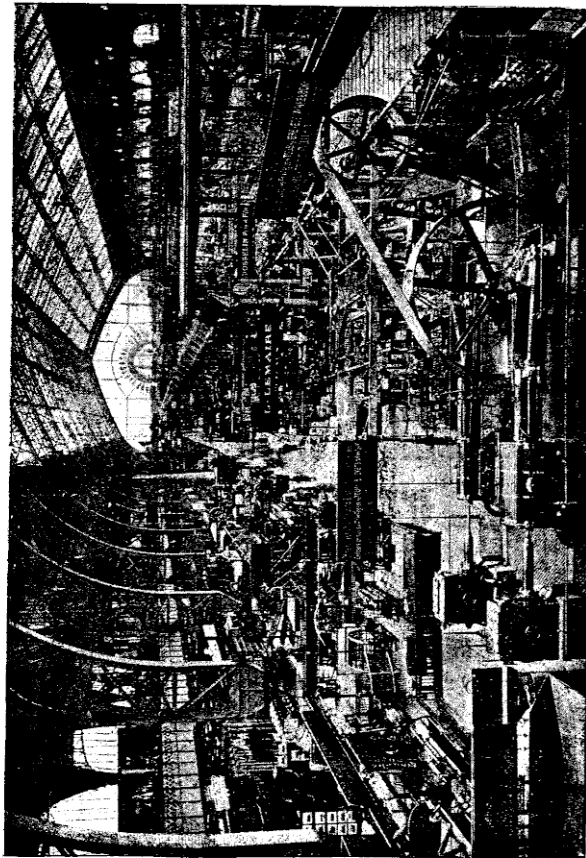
Vue intérieure avec les Machines en Mouvement.
